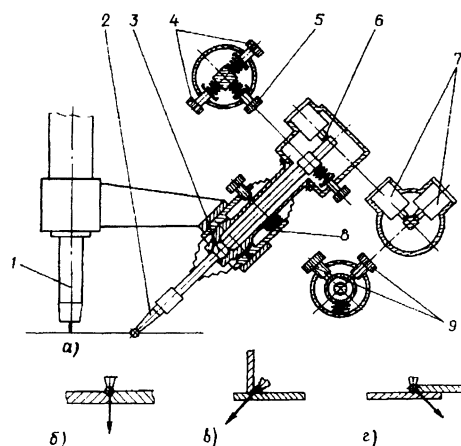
Схема двухкоординатного электромеханического датчика (*a*) и направления усилия копирования при сварке стыковых (*б*) и угловых (*в*, *г*) швов:
